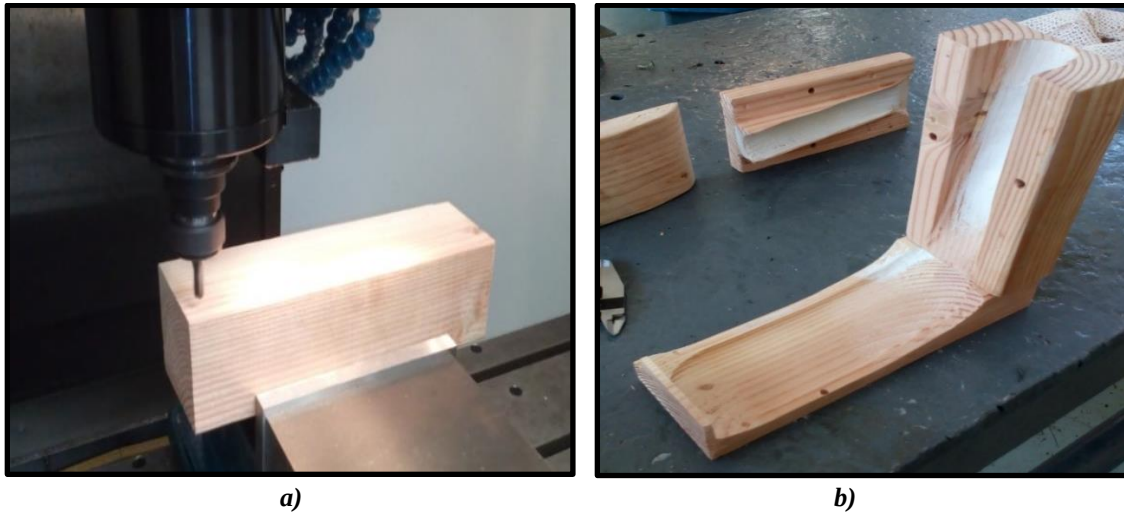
a) Maquinado de molde en CNC HAAS VF-9; b) Molde de madera en su etapa final.
